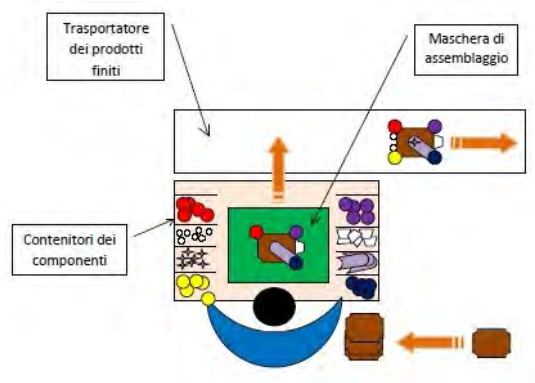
Layout di una postazione singola di assemblaggio manuale.
